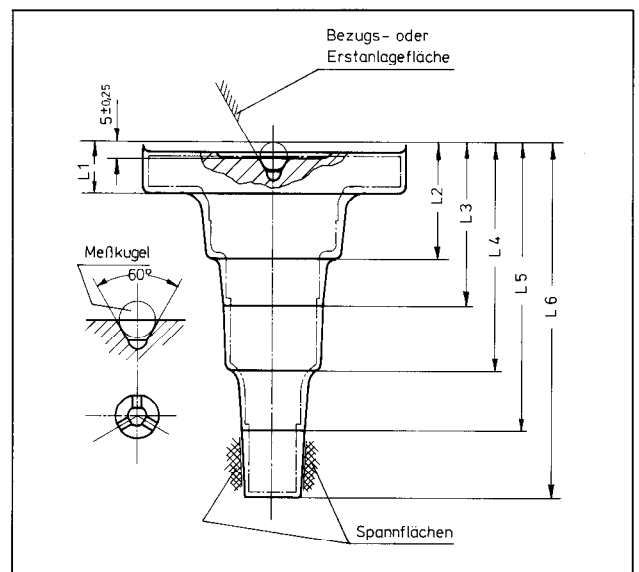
Ansicht einer Flanschswelle mit eingeschmiedeter Zentrierung
